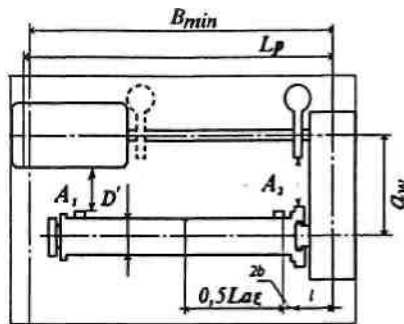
Компоновка механизма подъема с одним или двумя тормозами и промежуточным валом
